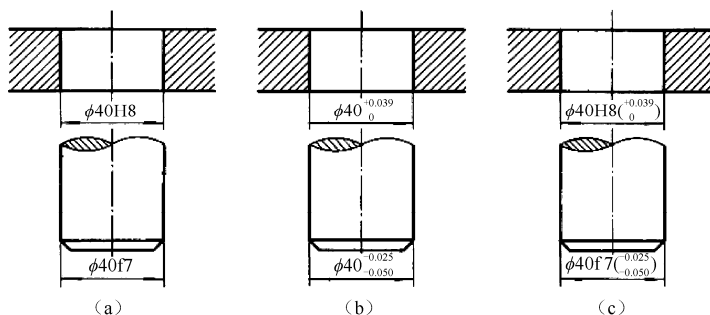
尺寸公差与配合在零件图中的标注实例
